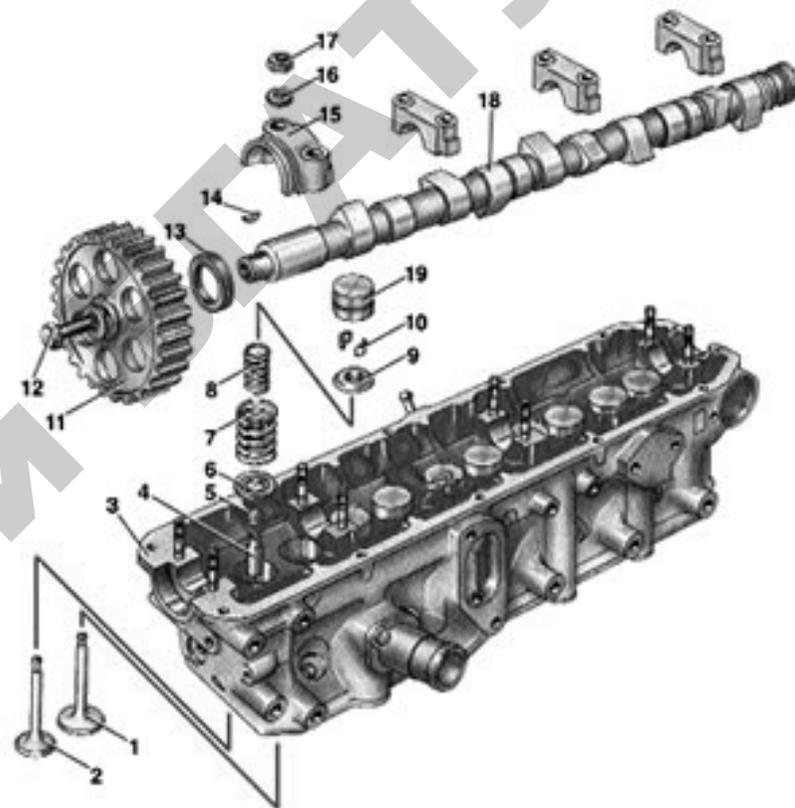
Головка блока цилиндров, распределительный вал и клапаны:
